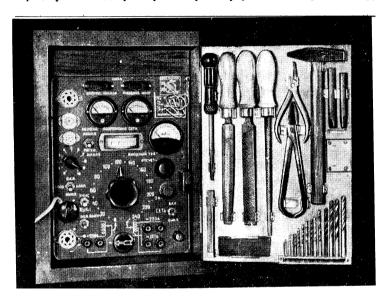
Слесарный инструмент на дверце правой тумбы.
